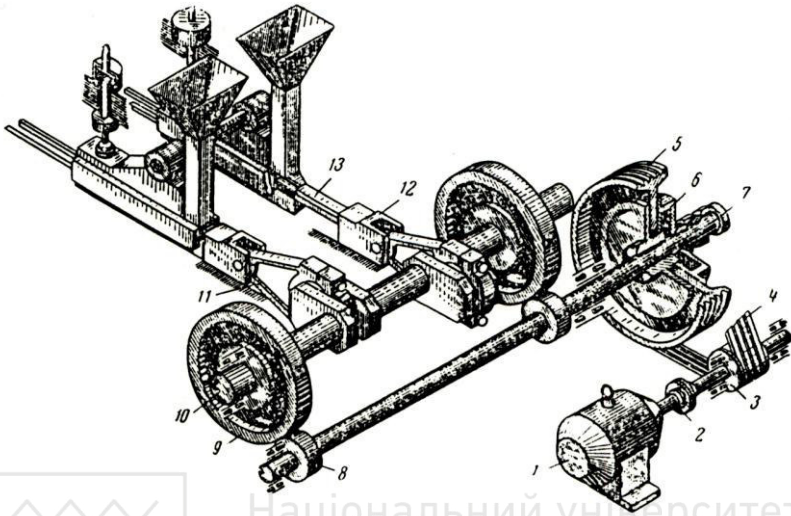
Кінематична схема преса Б8232: 1 – електродвигун; 2 – пружна муфта; 3 – ведучий шків клинопасової передачі; 4 – клинові паси; 5 – маховик; 6 – фрикційний запобіжний пристрій; 7 – приводний вал; 8 – косозубчасті шестерні; 9 – зубчасті колеса; 10 – колінчастий вал; 11 – шатунно-кривошипний механізм; 12 – повзун; 13 – штемпель
